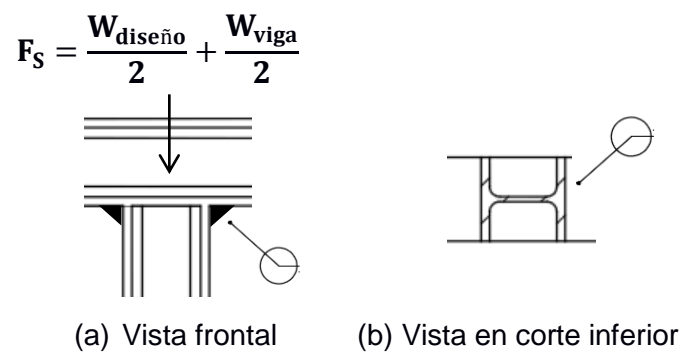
Fuerzas presentes en la unión de soldadura #1.
